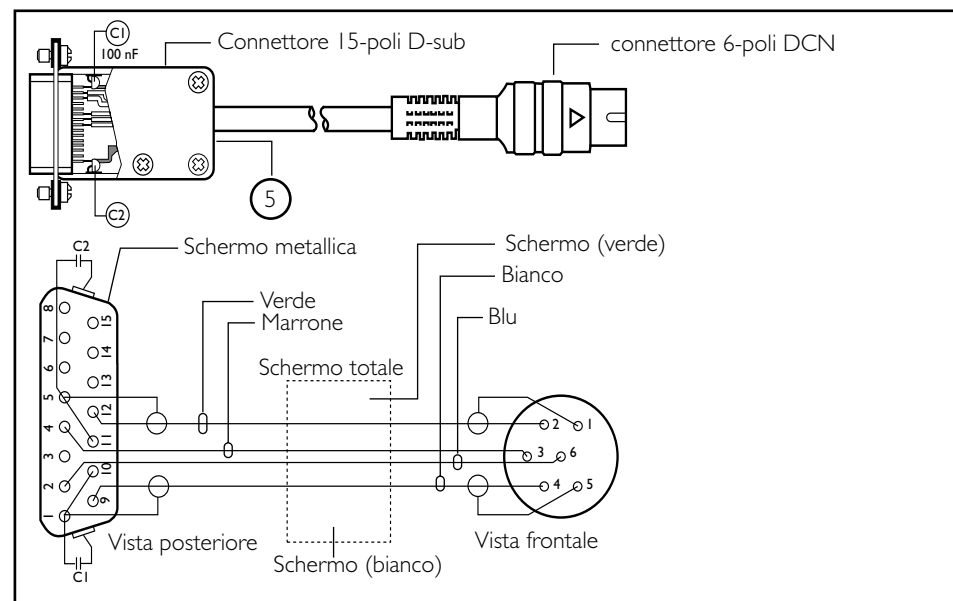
Collegamenti del Cablaggio di rete LBB 3510/00
